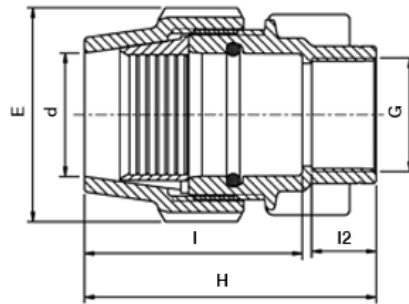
Plasson: Adaptador PEAD Compressão/Rosca – Corte longitudinal
